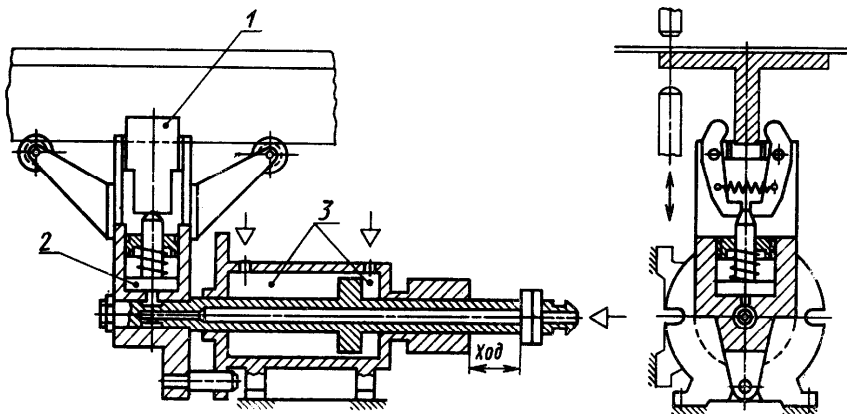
Устройство шаговой подачи при контактной сварке
